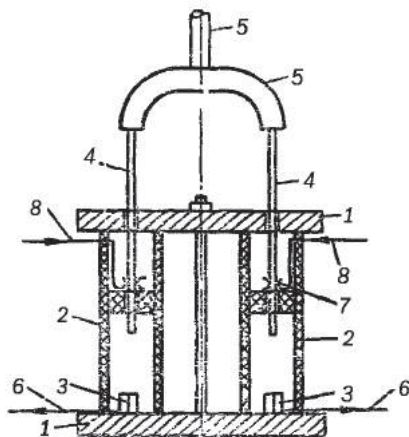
5 Трубчатый выключатель завода «Эрликон» (1898 г.)
